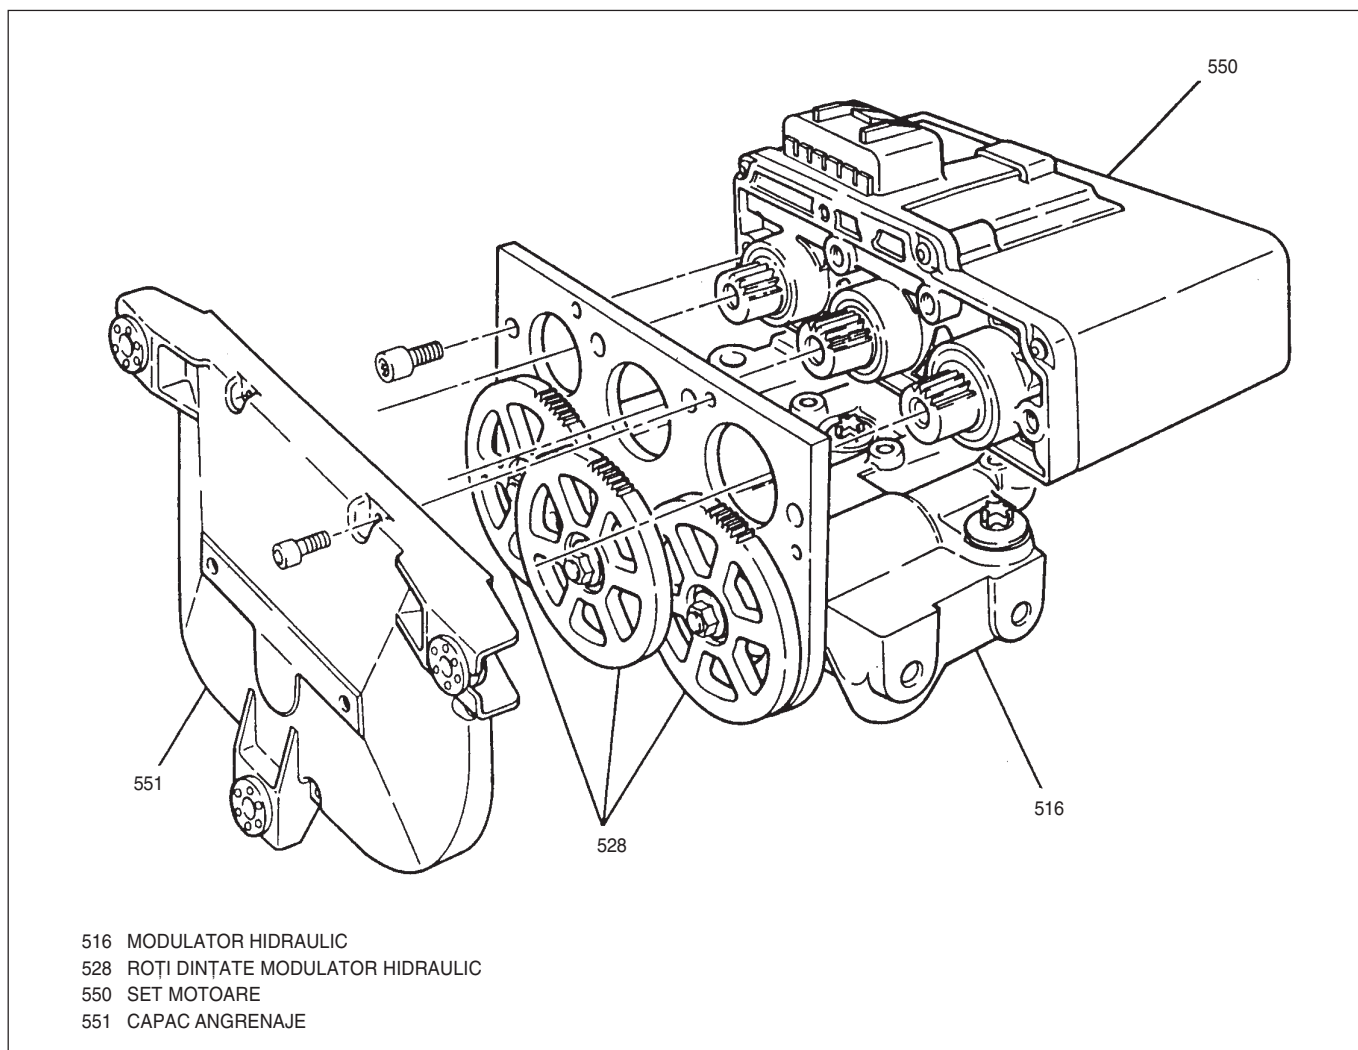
Ansamblu modulator hidraulic/set de motoare - vedere pe componente
